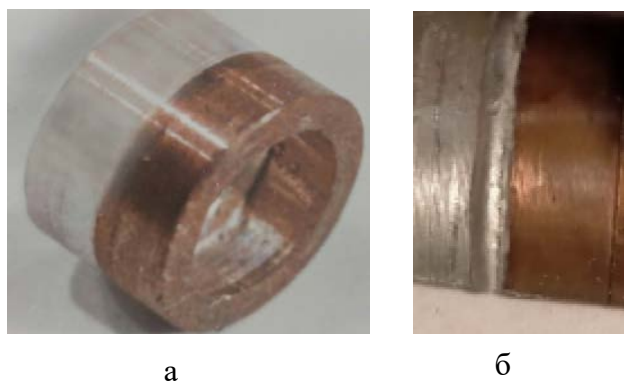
Переходник из алюминиевого сплава АД 31 и меди М3 (а) и внешний вид сварного соединения
